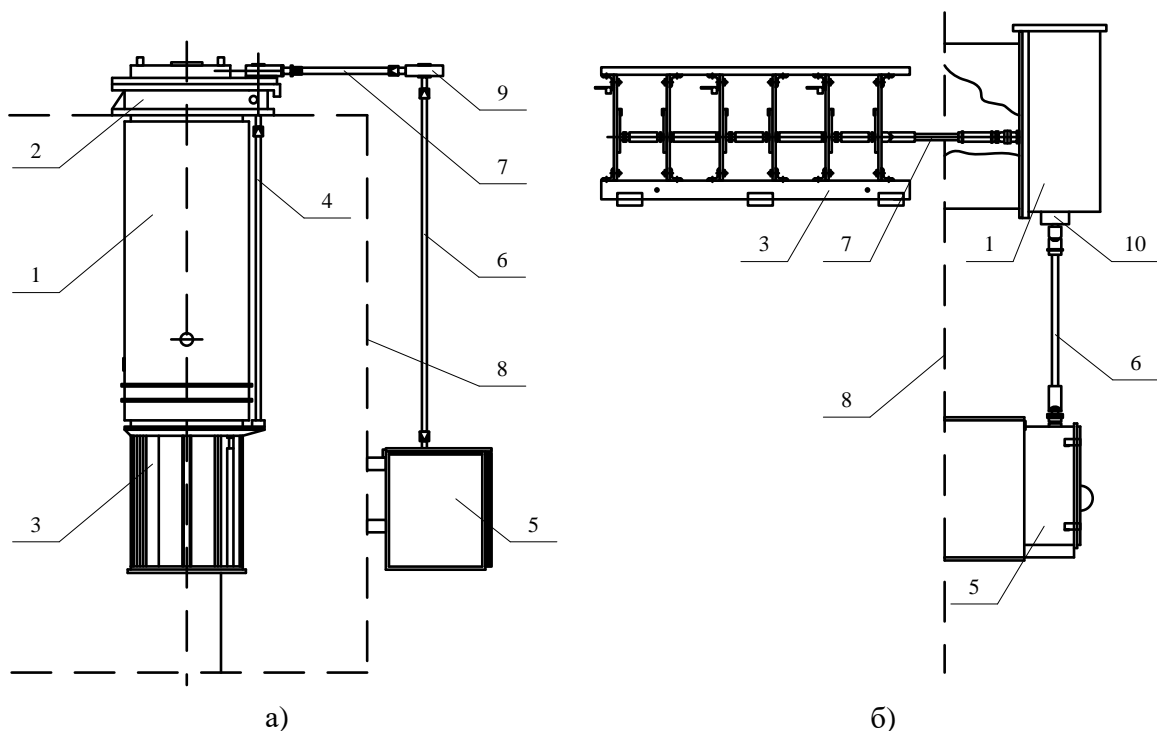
Схеми компоновки пристроїв РПН
